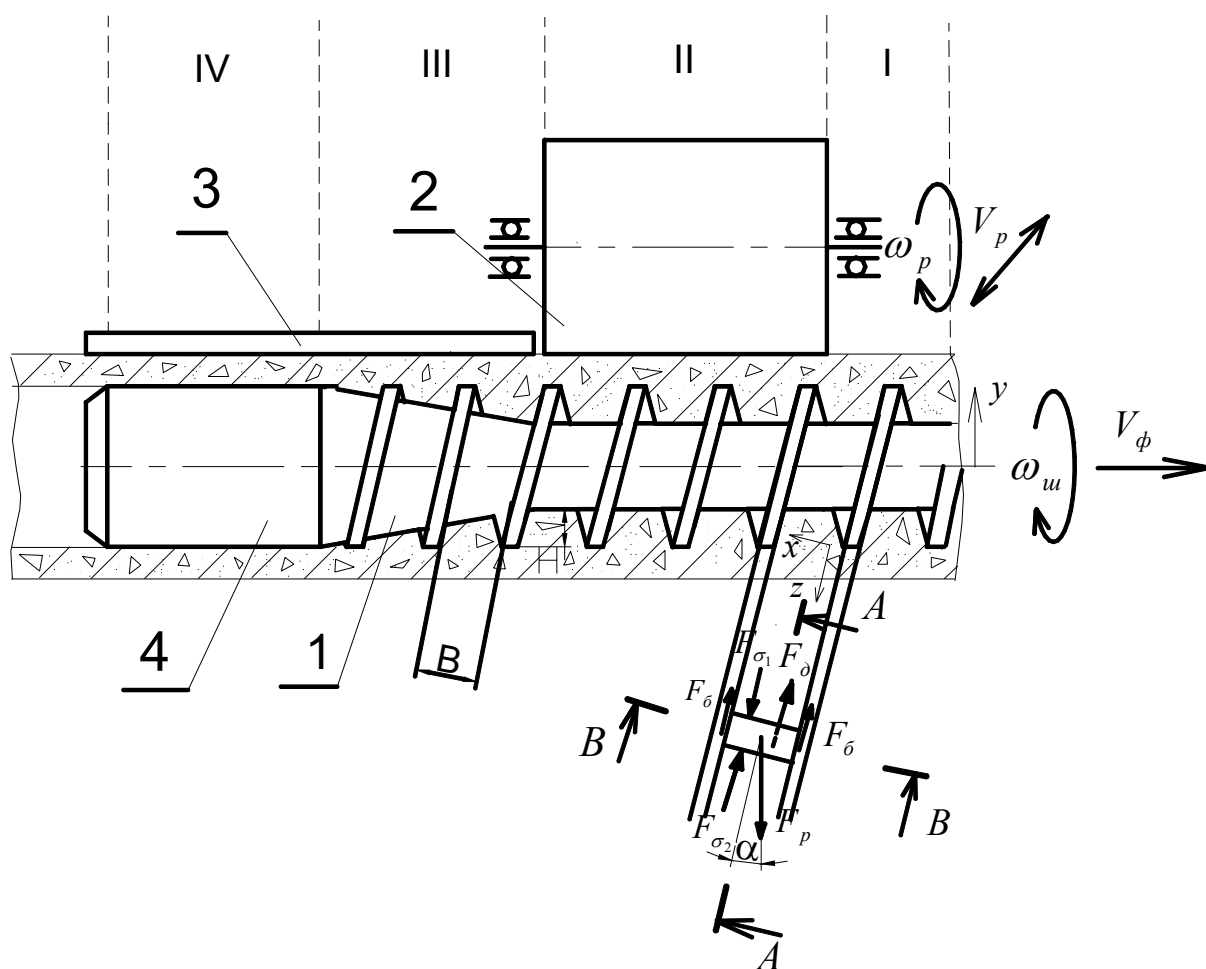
Розрахункова схема процесу ролико-екструзійного формування
